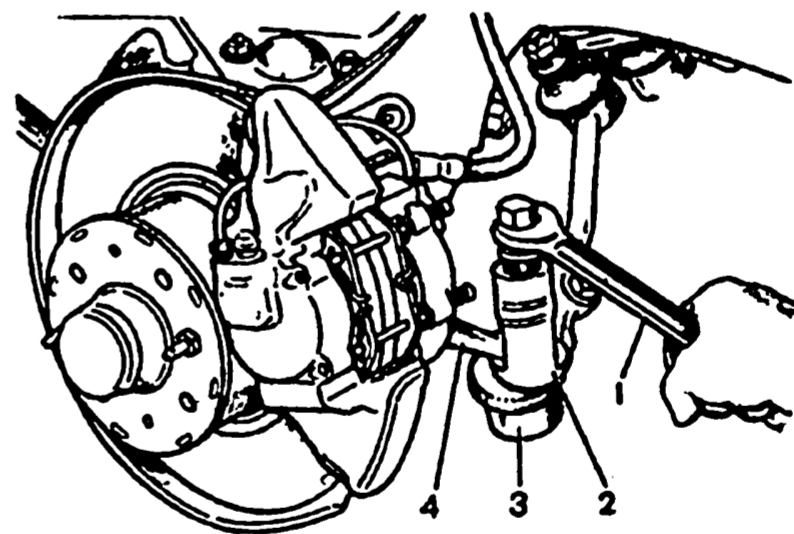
Снятие шаровых пальцев тяг рулевой трапеции: 1 - ключ гаечный; 2 - съемник А.47052; 3 - шаровой шарнир; 4 - рычаг поворотного кулака
